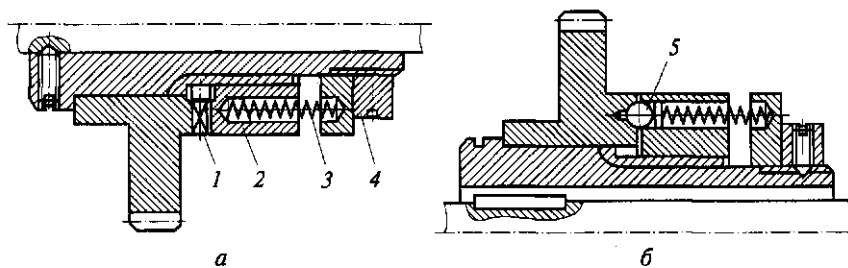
Кулачковая (*а*) и шариковая (*б*) предохранительные муфты: 1 — кулачки; 2 — подвижный элемент; 3 — пружина; 4 — гайка; 5 — шарик
